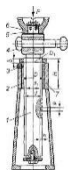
Винтовой домкрат: 1—винт; 2 — гайка; 3 — стопорный винт; 4 — рукоятка; 5 — чашка домкрата; 6— шип, 7 — корпус
